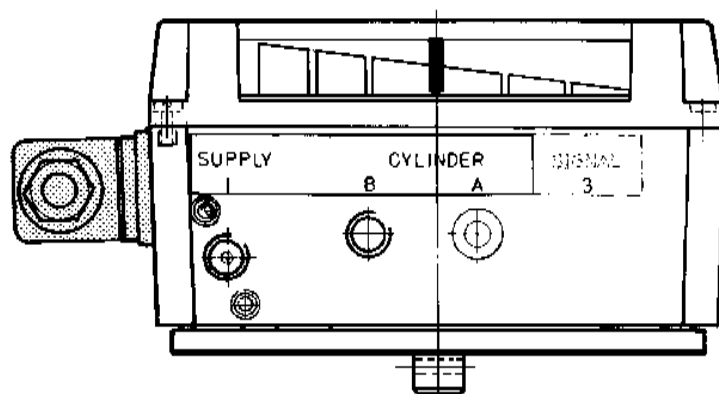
Детализированный чертёж NAF 370210, пневматического позиционера клапана
